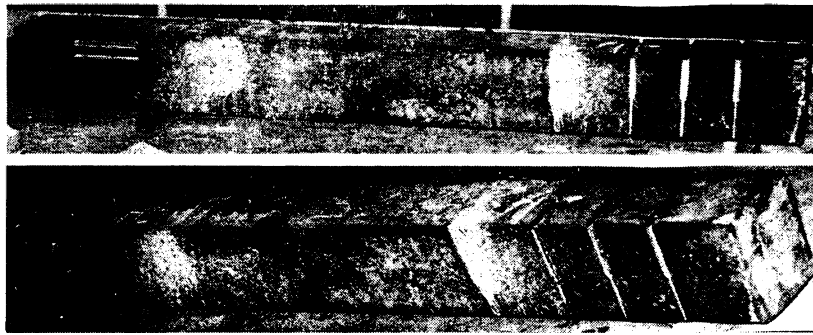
Непрерывнолитая заготовка сечением 250×300×2470 мм с нанесенными искусственными поверхностными дефектами
